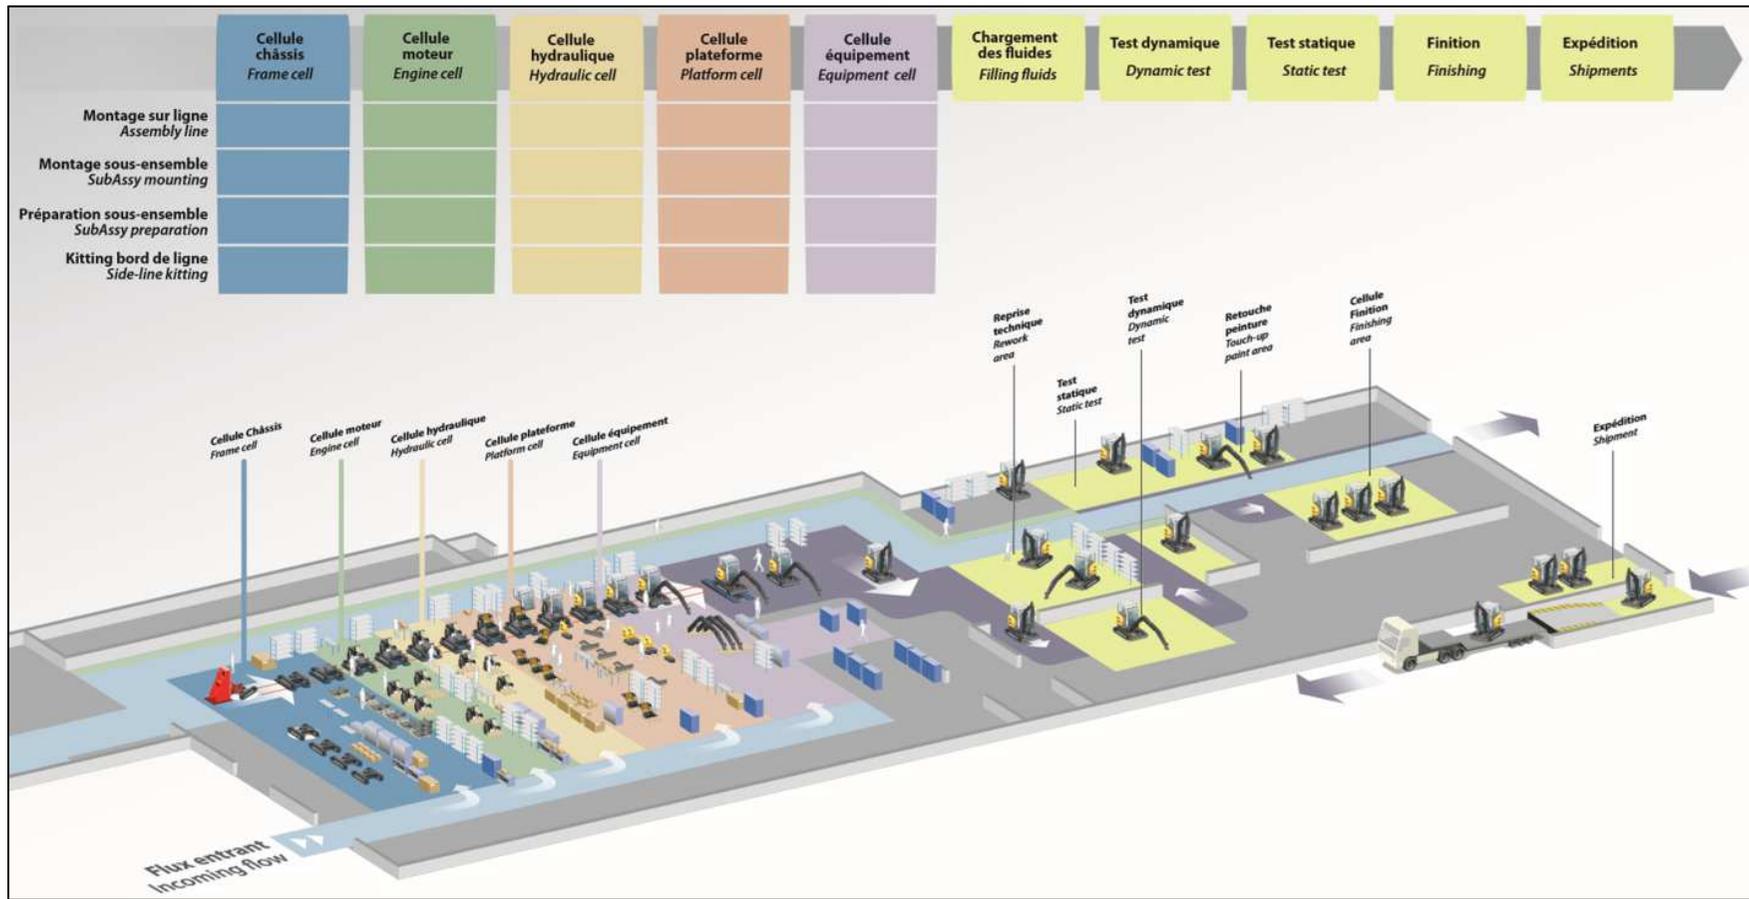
Plan de l'atelier d'assemblage de l'entreprise partenaire
